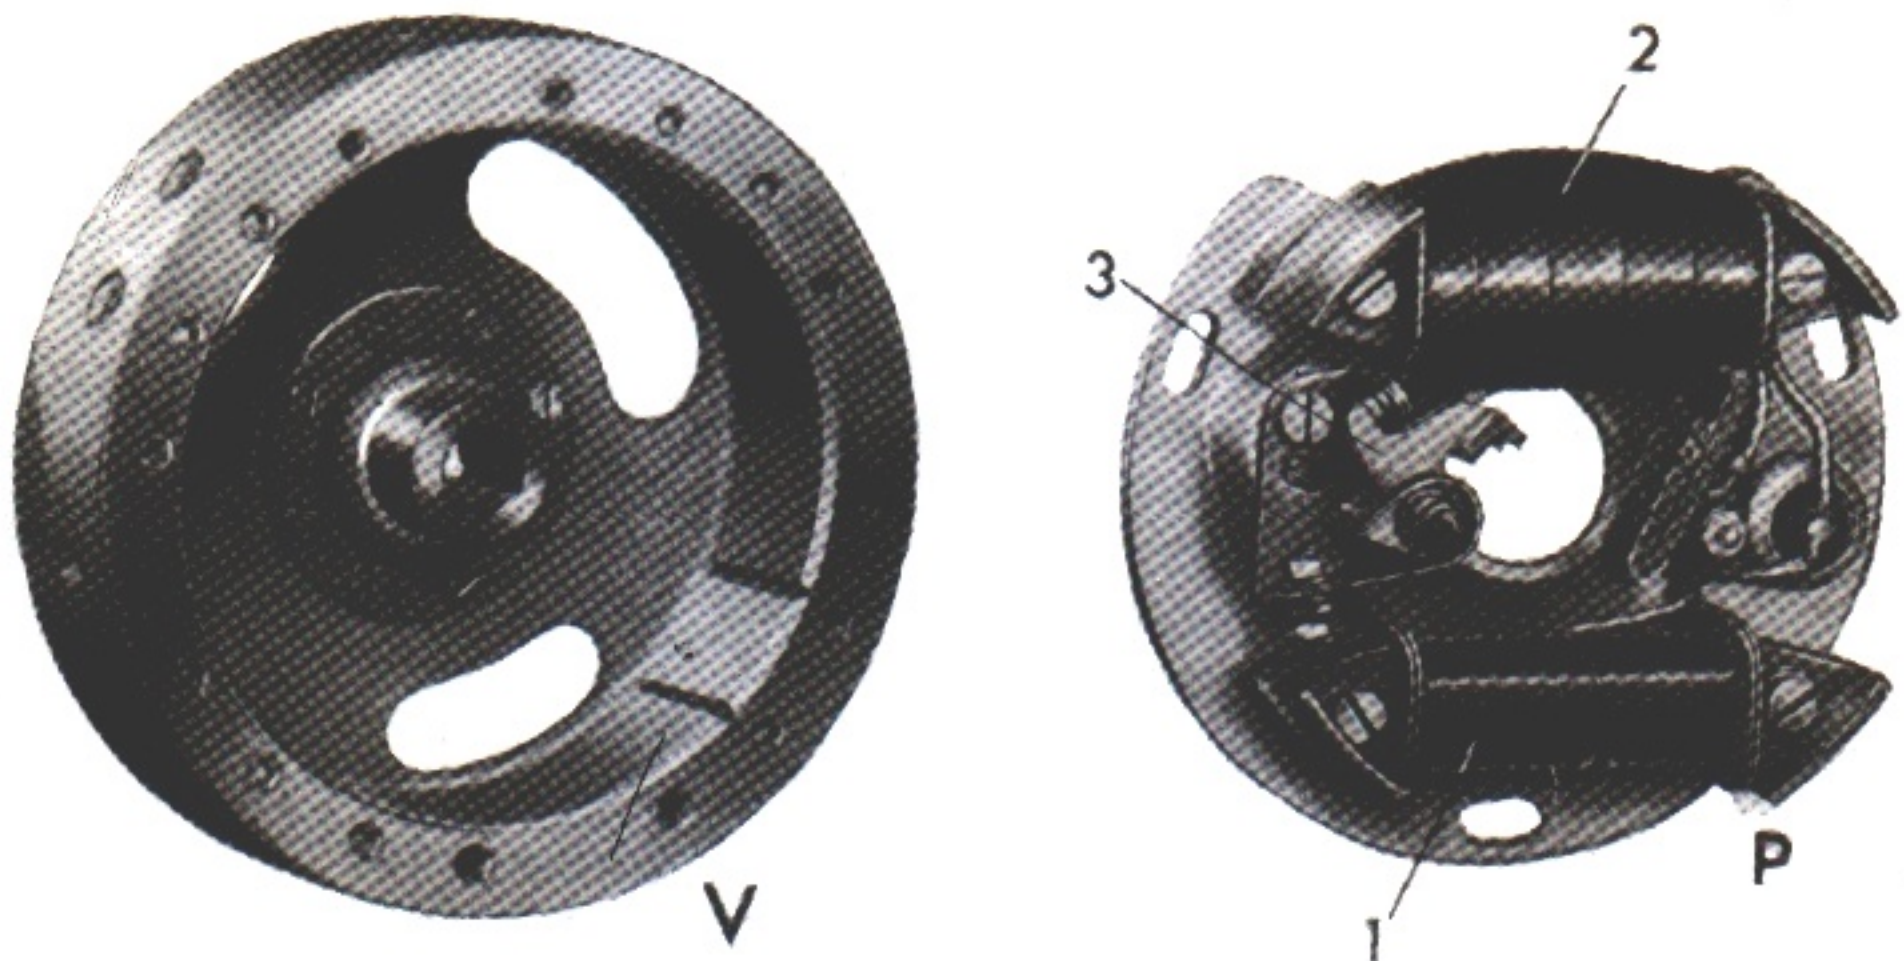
Vistas de las dos piezas fundamentales de que se compone un volante magnético. V, volante rotor; P, plato base fijo. 1, bobina de alumbrado; 2, bobina de encendido; 3, platinos.
